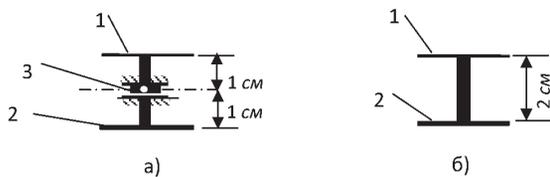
Варианты жестких перемычек: а – перемычка со сдвиговым компенсатором; б – обычная перемычка; 1 – трубопровод – сердечник; 2 – трубопровод – рубашка; 3 – сдвиговой компенсатор (боковой ползун)
